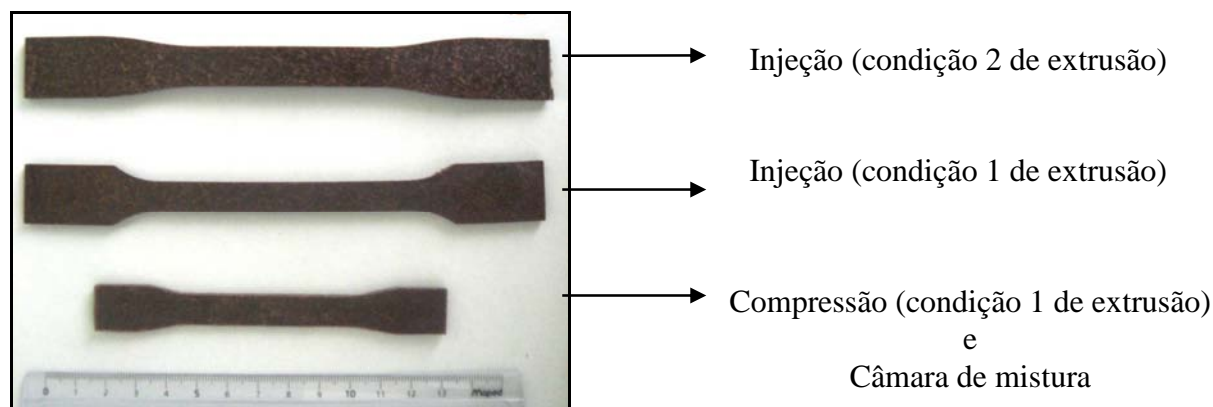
Corpos de prova obtidos pelos diferentes processos de moldagem
